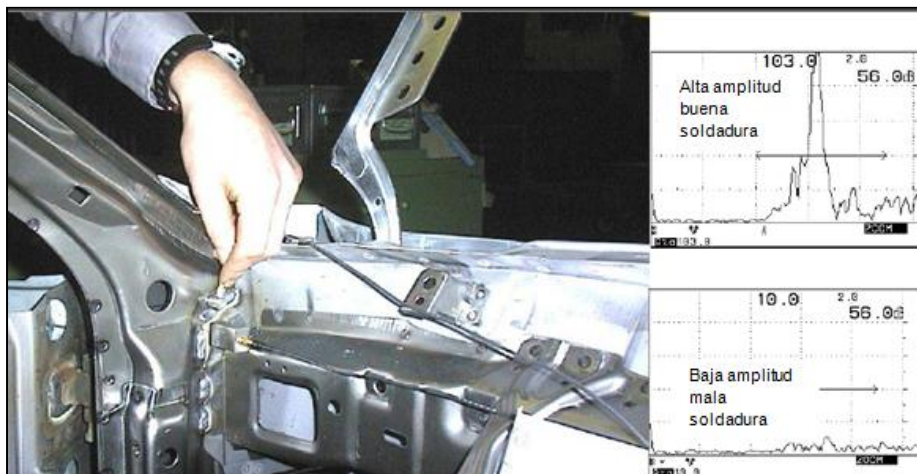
Inspección de soldaduras de carrocería [7]
